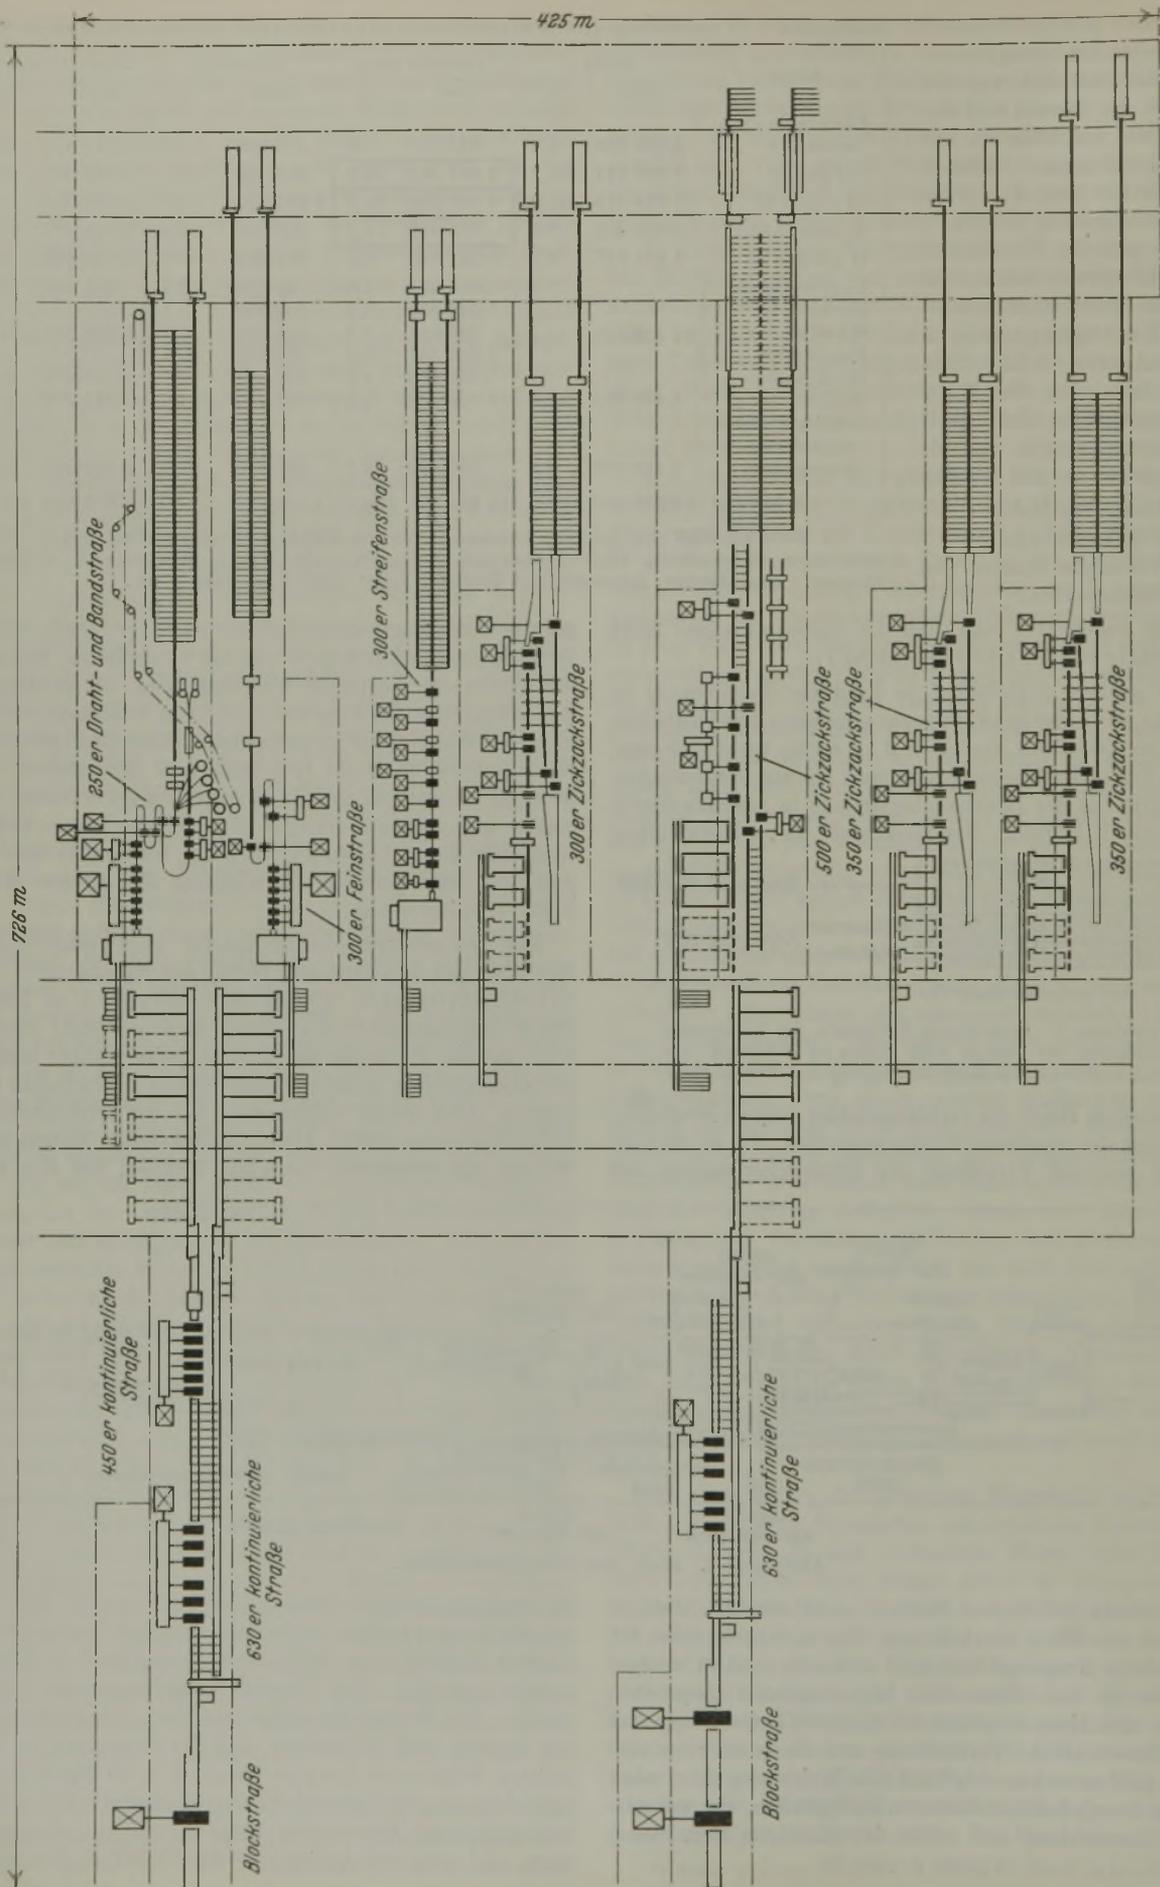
Gesamtplan einer neuen Walzwerksanlage.
